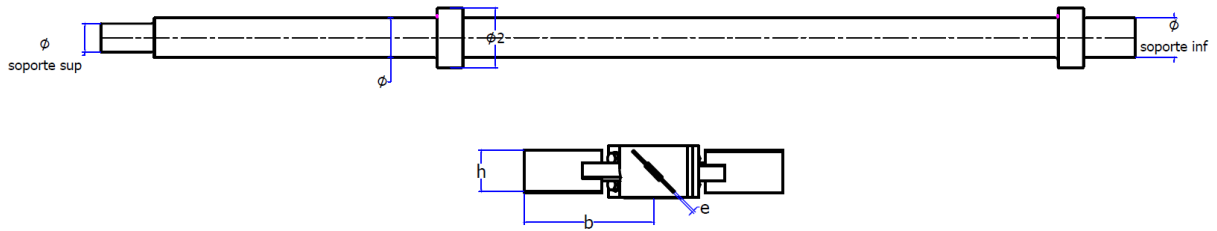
Plano de dimensiones del eje y hélices del tanque agitador
